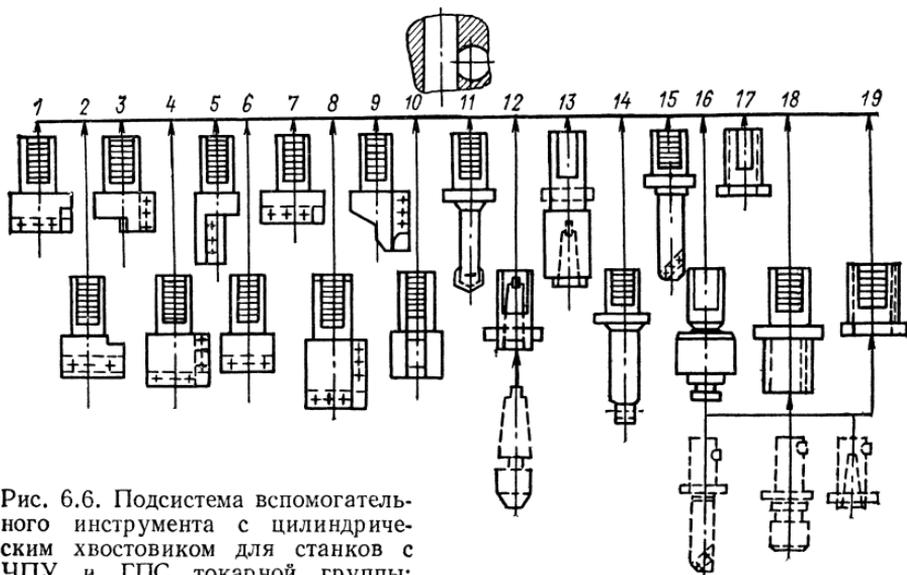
Подсистема вспомогательного инструмента с цилиндрическим хвостовиком для станков с ЧПУ и ГПС токарной группы:
